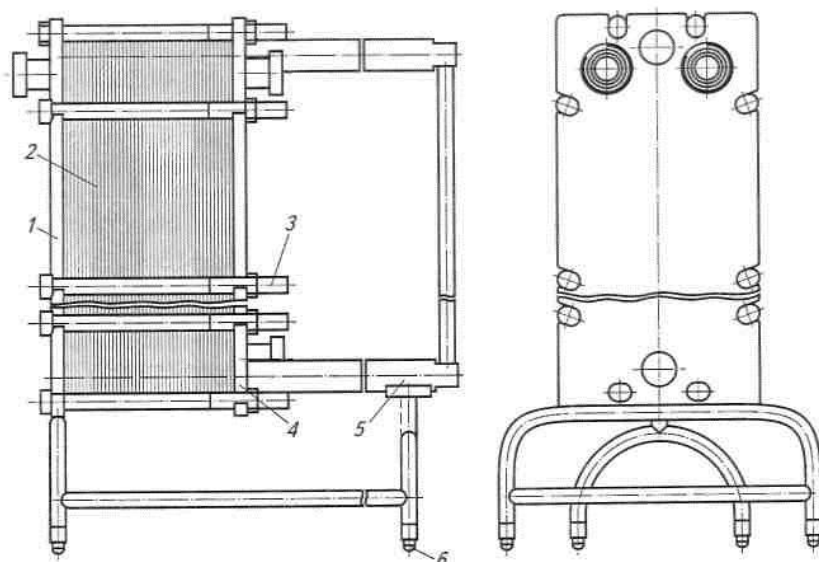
Односекционный пластинчатый нагреватель молока: 1 — станина; 2 — пластины; 3 — зажимная стяжка; 4 — нажимная плита; 5 — направляющая штанга; 6 — ножка.
